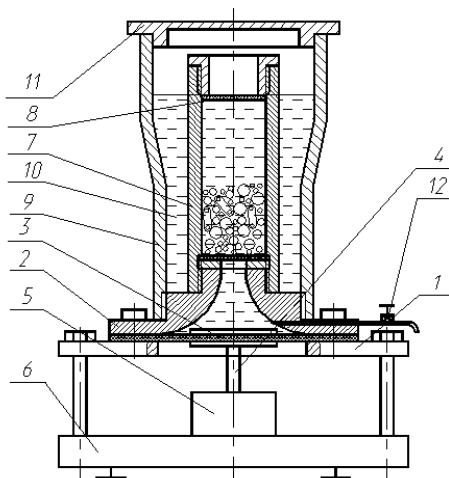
Вібраційна машина для об'ємної струмино-абразивного оброблення задирок : 1 – плита; 2 – камера; 3 – мембрана; 4 – шток; 5 – вібропривод; 6 – основа; 7 – ємкість; 8 – сітка; 9 – циліндрична ємкість; 10 – рідина; 11 – кришка; 12 – кран
